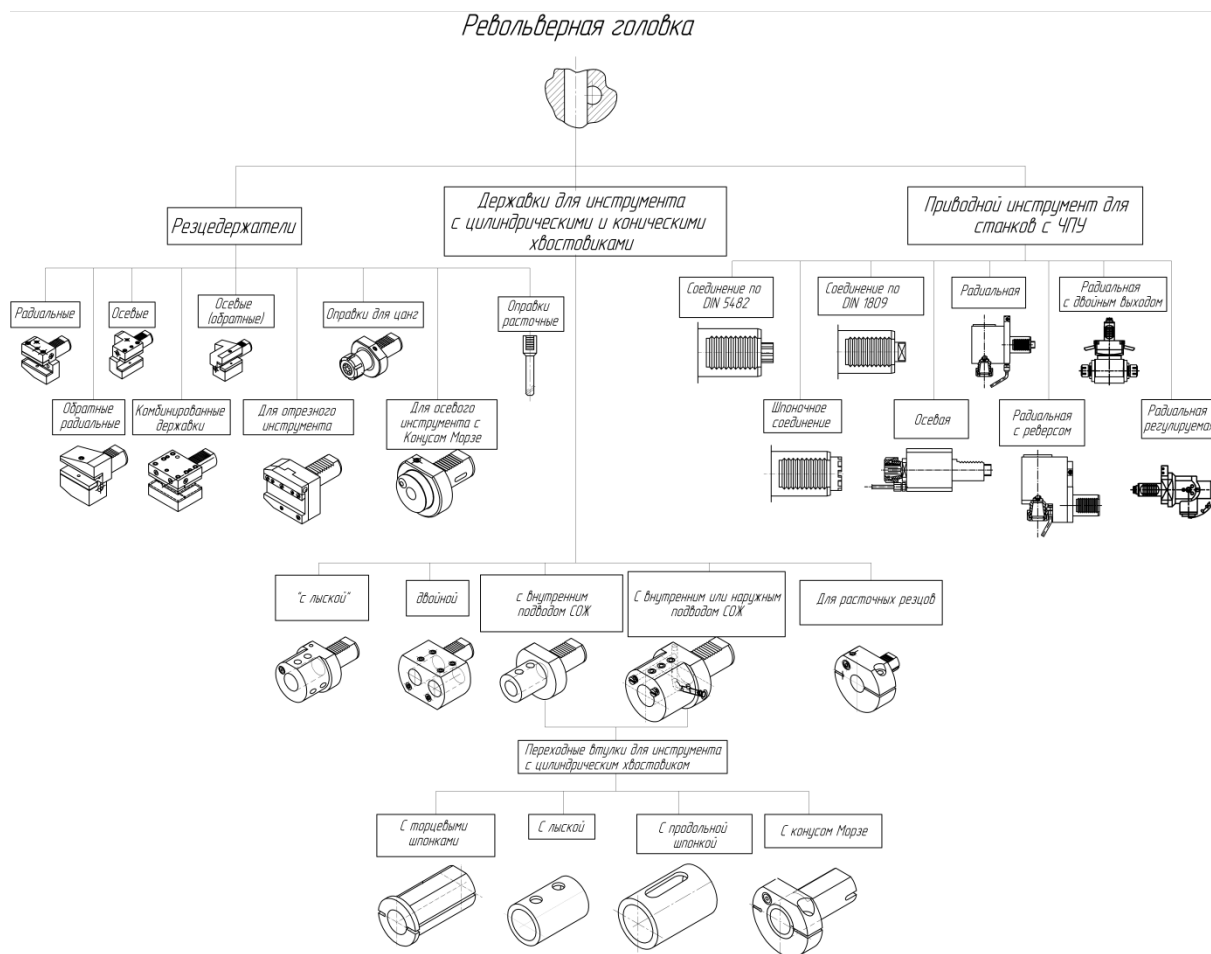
Логистическая схема выбора вспомогательного инструмента для станков с ЧПУ токарной группы
